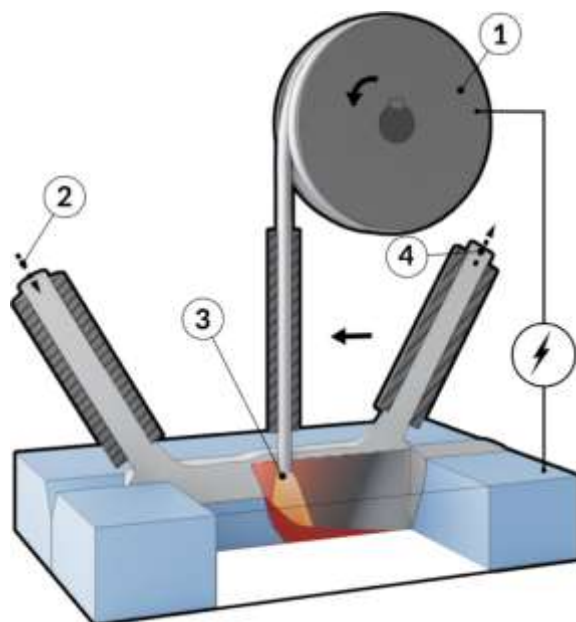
Схема автоматичного зварювання під флюсом
